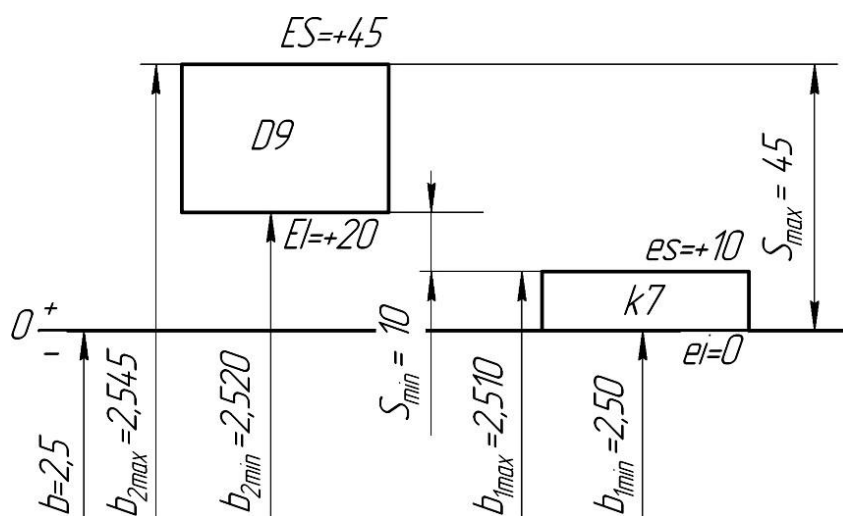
Схема расположения полей допусков ширины шлица
